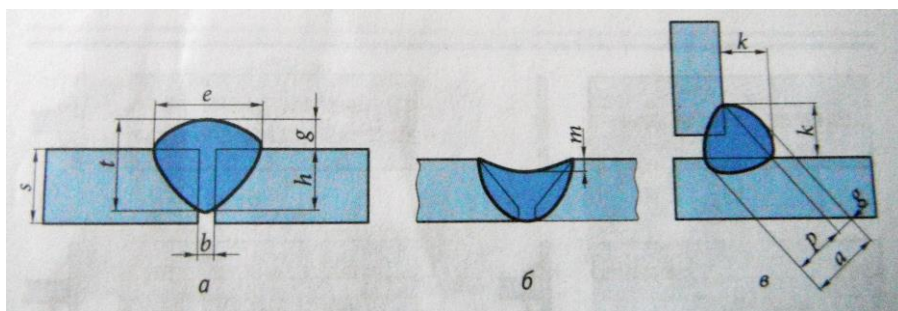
Основные геометрические параметры стыковых и угловых сварных швов.
